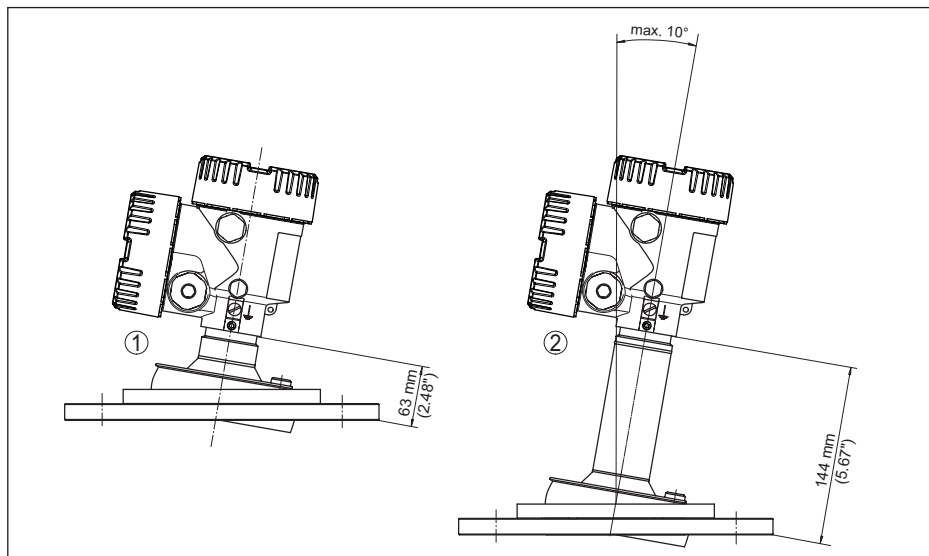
NCR-86, flange com antena lentiforme e suporte giratório
